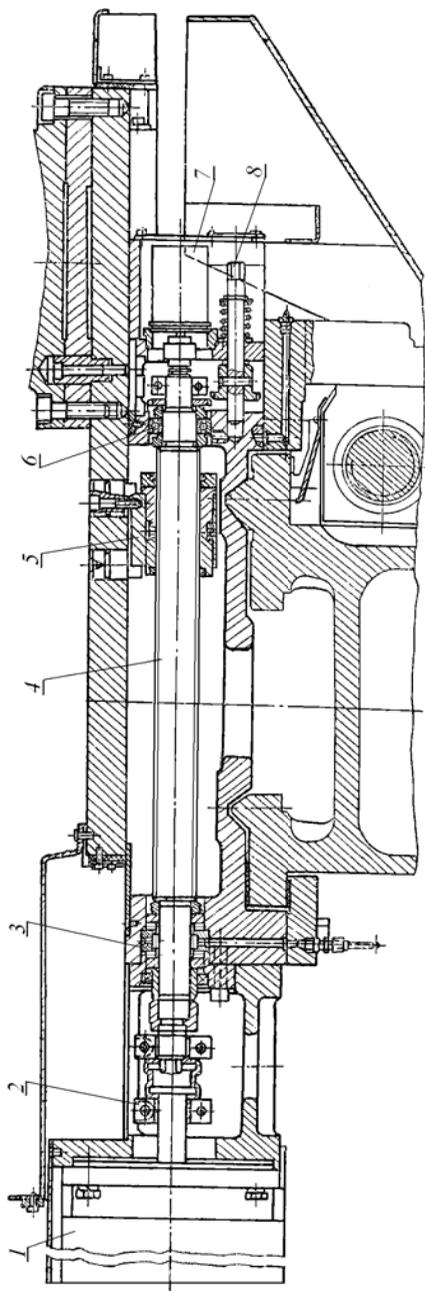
Привод поперечной подачи суппорта токарного станка с ЧПУ модели 16A20Ф3 :
